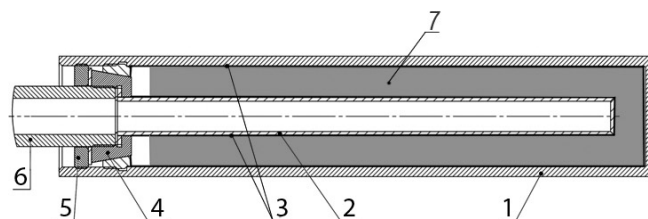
Общий вид конструкции малогабаритной ампулы реперной точки олова конструкции ВНИИМС
